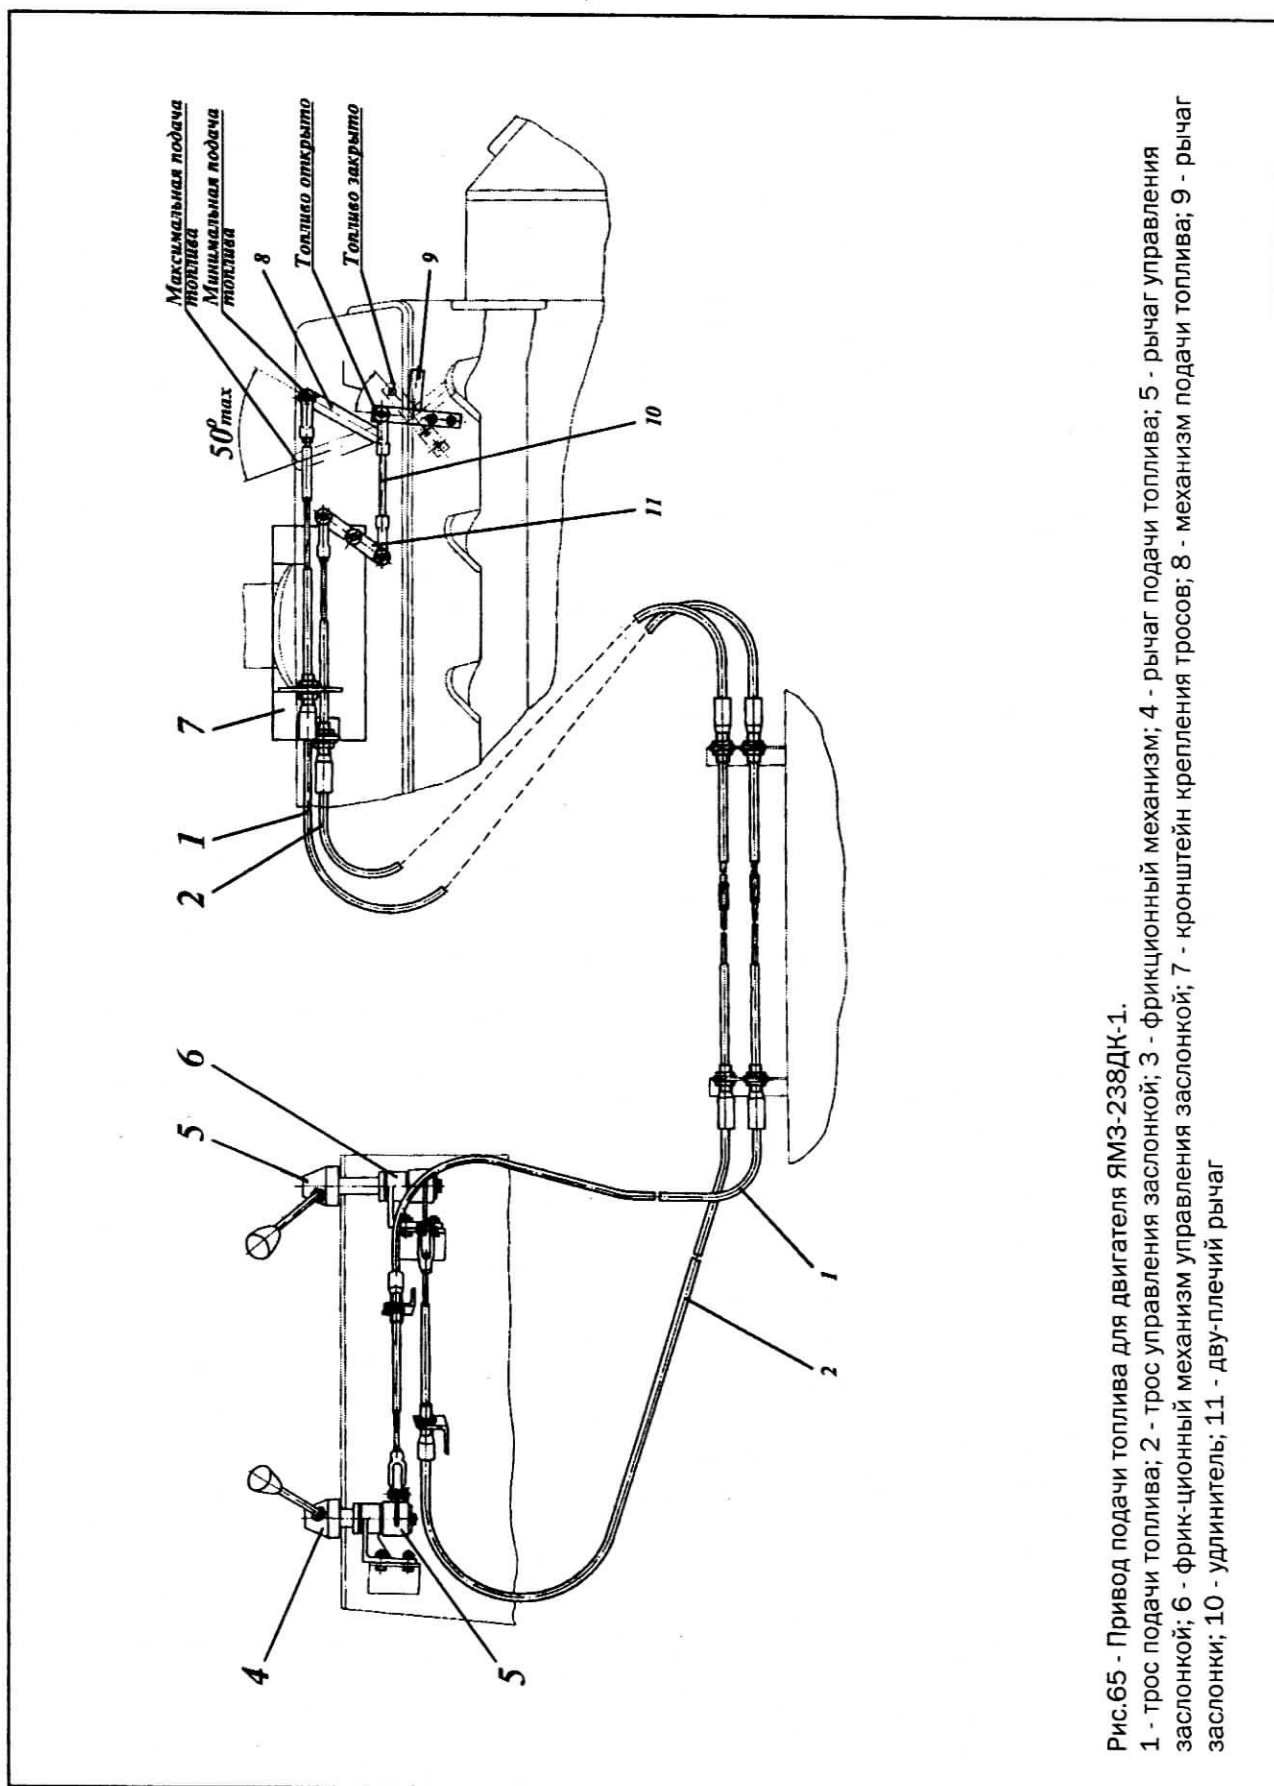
Привод подачи топлива для двигателя ЯМЗ-238ДК-1.
